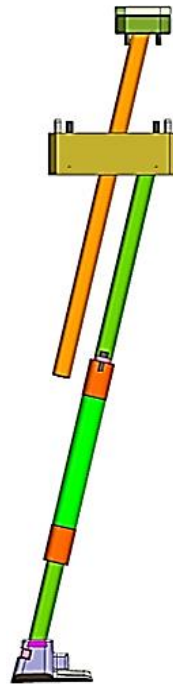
Movimento à extração de duplo veio para desmoldagem superior a 10°
